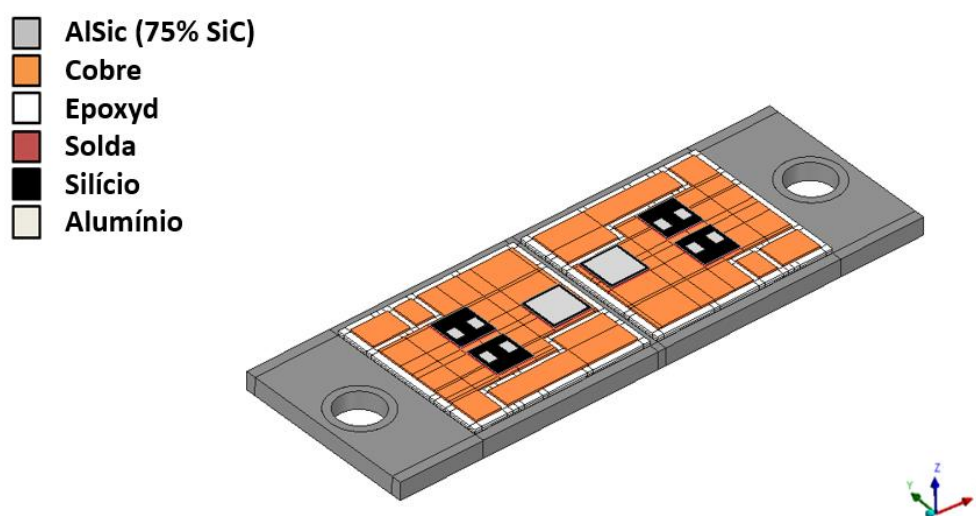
Geometria CAD da Base (AlSiC), camada de cobre, isolante térmico (Epoxyd), solda, pads (alumínio), chip IGBT e chip Diodo (Silício) e indicação dos materiais constituintes.
